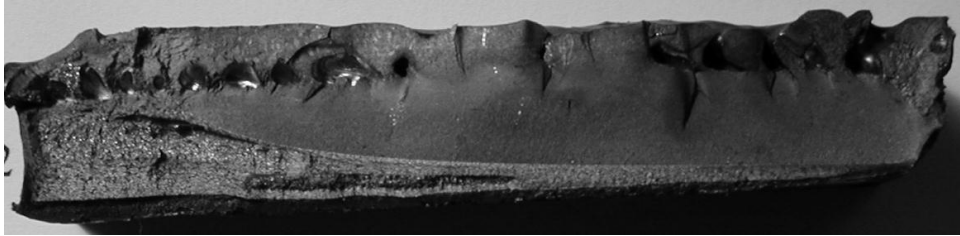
Macrografia da superfície de fractura do provete PDR2.
